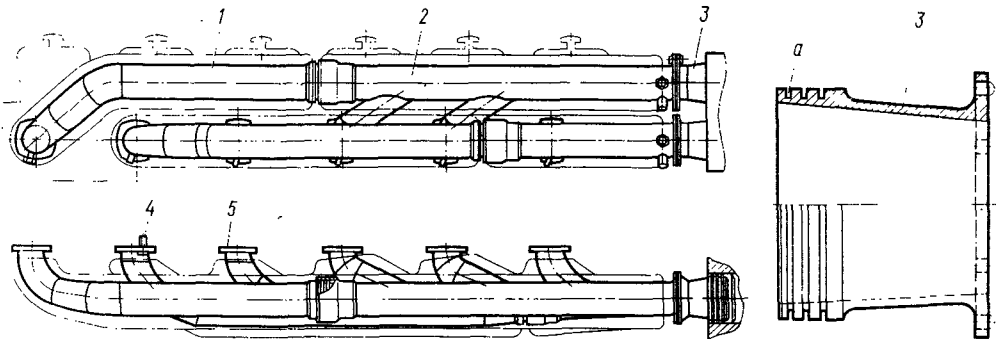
Выпускные коллекторы: 1, 2 — части коллектора; 3, 5 — патрубки; 4 — болт; а — канавка
